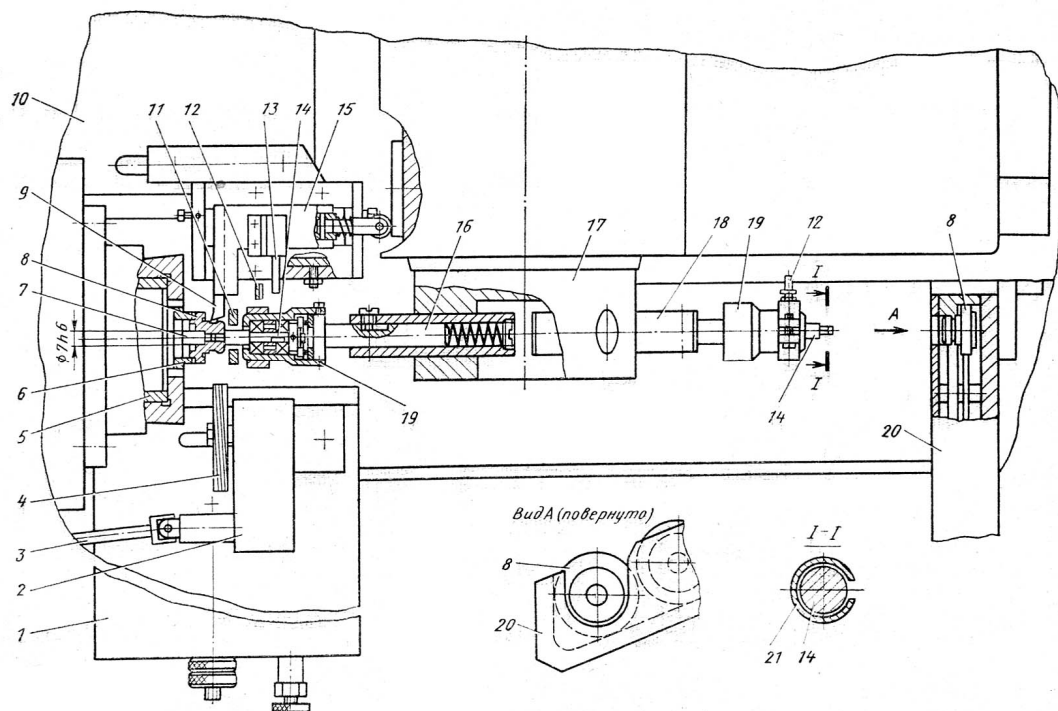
Токарно-револьверний автомат мод. 1Д118, налаштований на виконання допоміжних операцій на штучній заготовці
